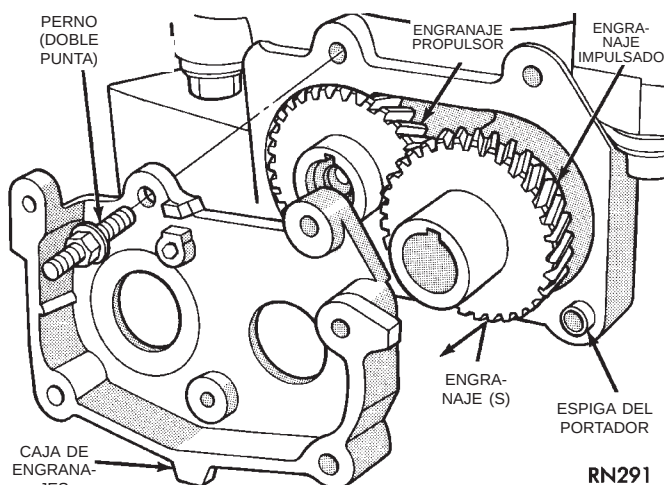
Caja de engranajes y engranajes PORTADOR DEL EJE REGULADOR
